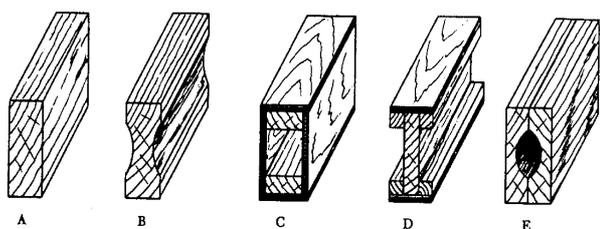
Configuração das seções em corte de longarinas típicas de madeira.
